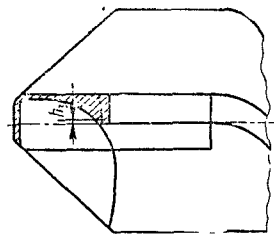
Износ сверла, оснащенного пластинкой твердого сплава
